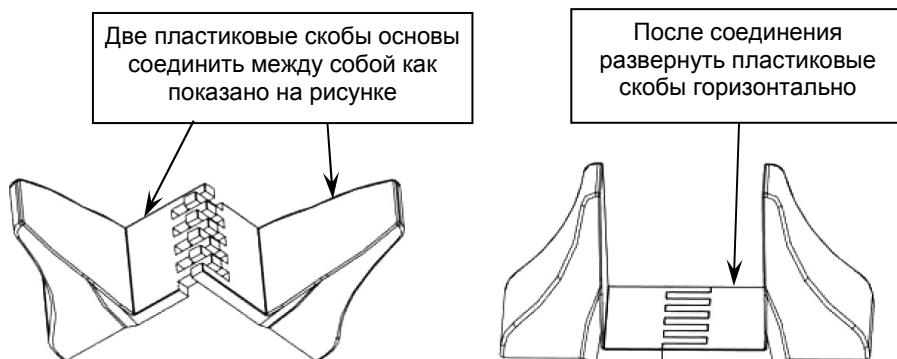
Сборка пластиковых основ для вертикальной установки изделия
